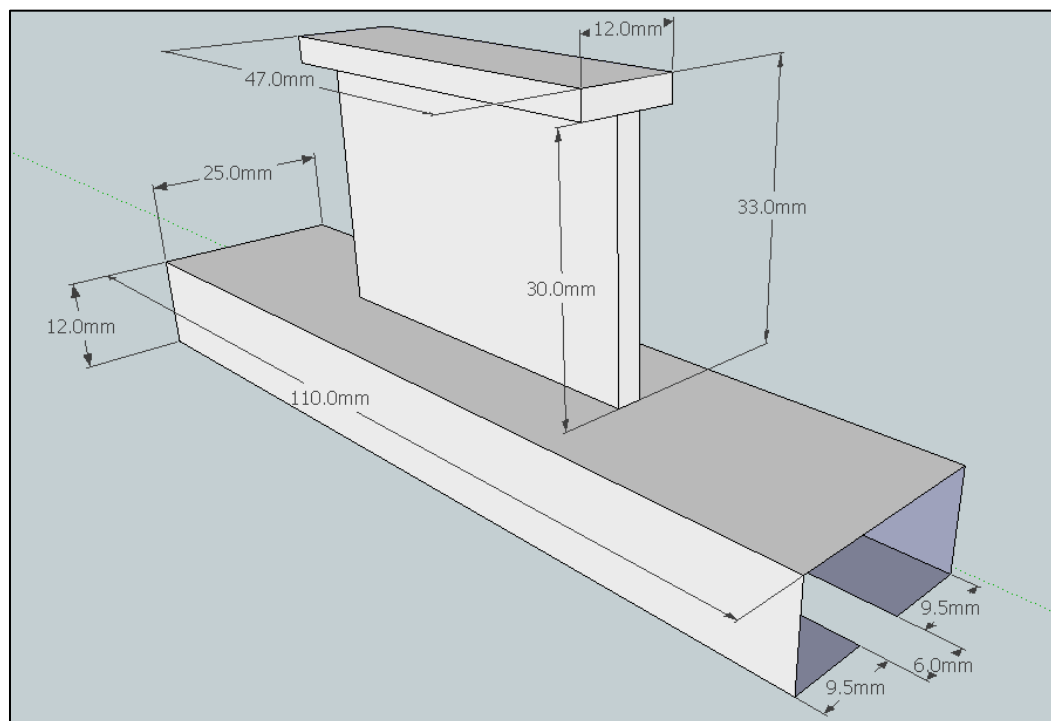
Dimensiones del puente que sostiene a los sujetadores.
